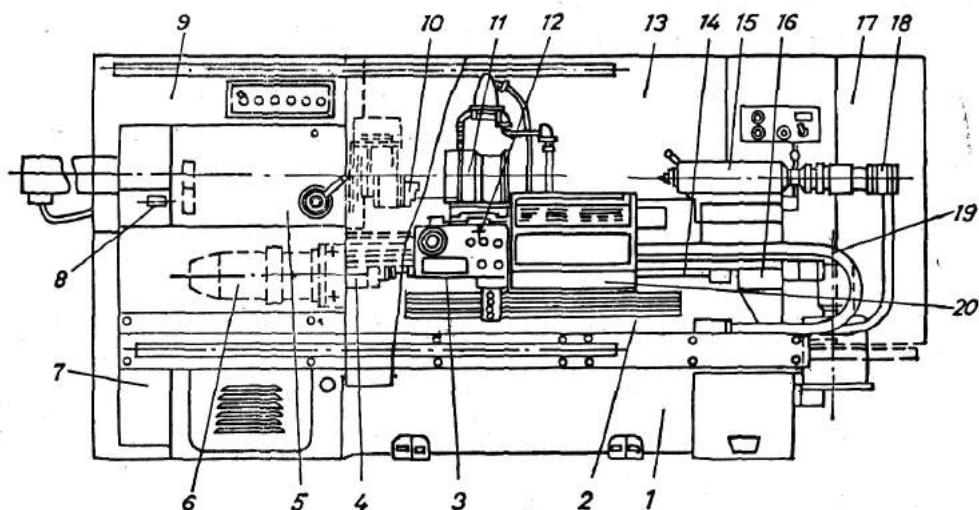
Токарний верстат з оперативною системою ЧПК моделі 16K20T1: 1 — основа; 2 — станина; 3 — каретка; 4 — ліва опора поздовжнього гвинта; 5 — шпиндельна бабка; 6 — привод поздовжнього переміщення; 7 — передня бабка; 8 — датчик різнарізання; 9 — шафа керування; 10 — шпиндельний вузол; 11 — поворотна револьверна головка; 12 — пульт керування; 13 — нерухома огорожа; 14 — гвинтова кулькова пара; 15 — задня бабка; 16 — права опора поздовжнього гвинта; 17 — електромеханічний привід пінолі задньої бабки; 19 — каретка; 20 — рухома огорожа.
